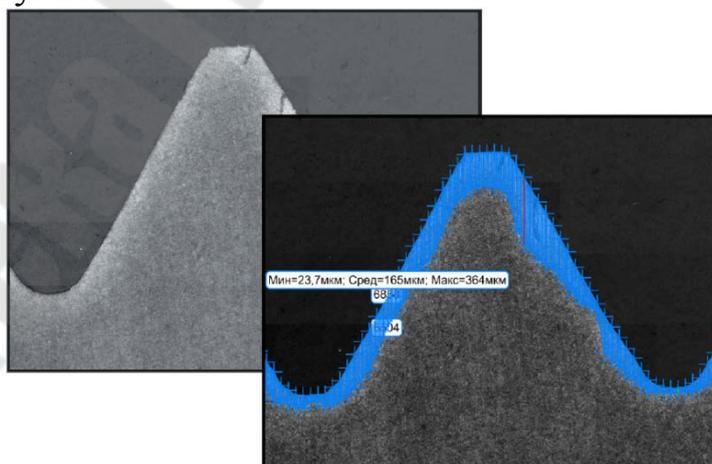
Обезуглероженный слой на поверхности зуба фрезы.
